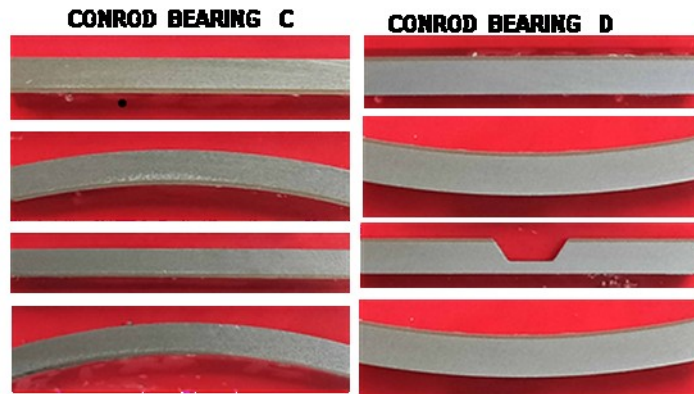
Sampel Uji kekerasan *conrod bearing* yang rusak
